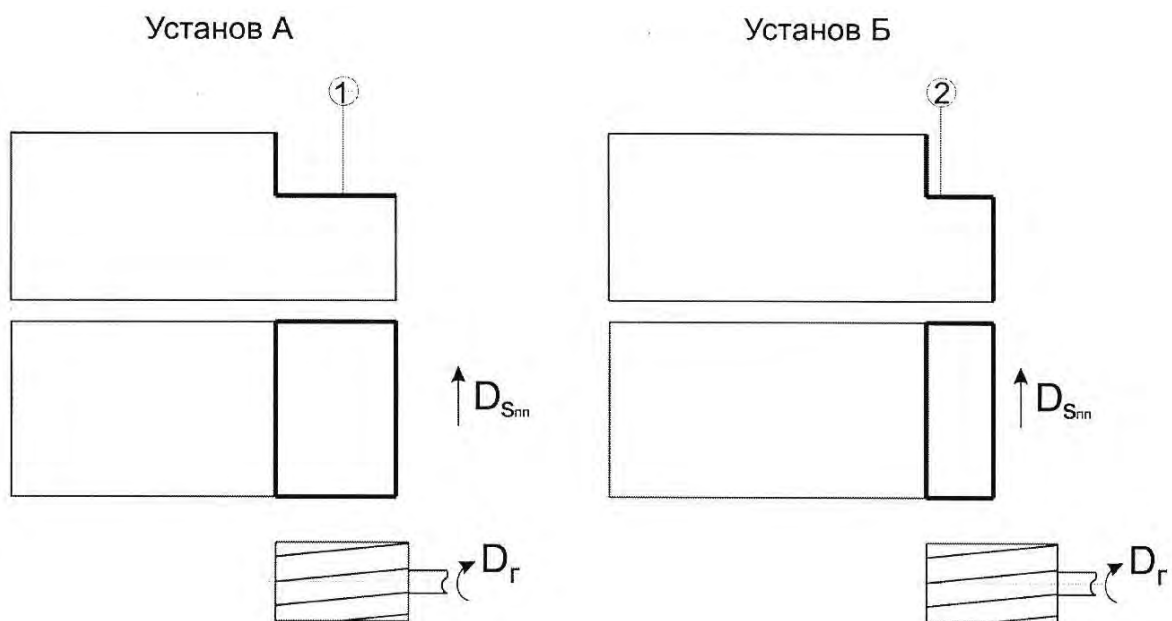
Эскизы обработки на горизонтально-фрезерной операции за два установка
